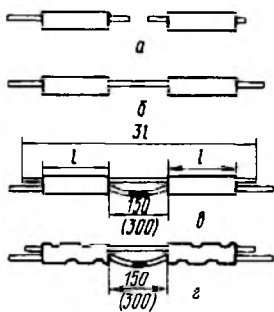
Соединение алюминиевых и сталеалюминиевых проводов термитной сваркой:
